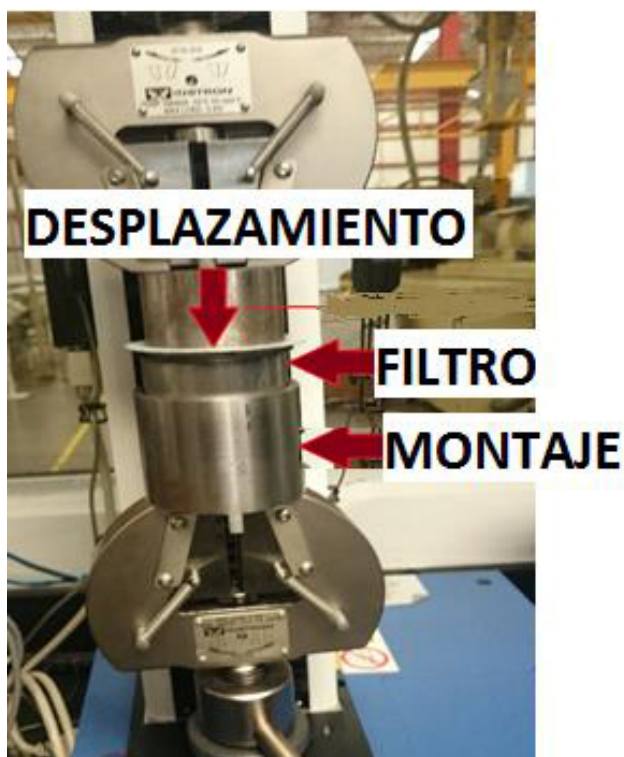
Montaje para realizar prueba de cerrado del filtro de aceite.
